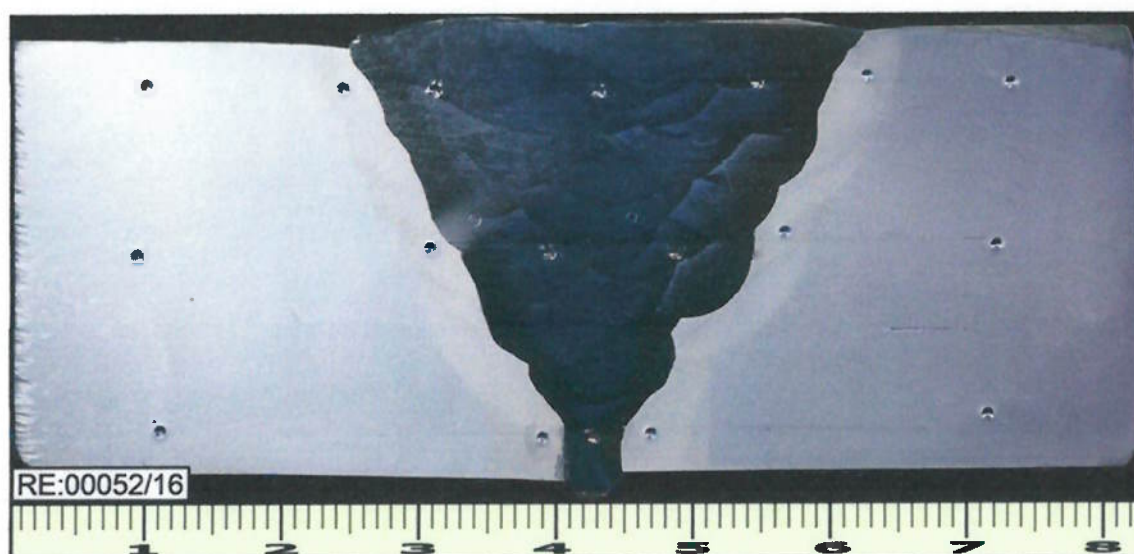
Macrografia da seção transversal do corpo de prova soldado com arame sólido
